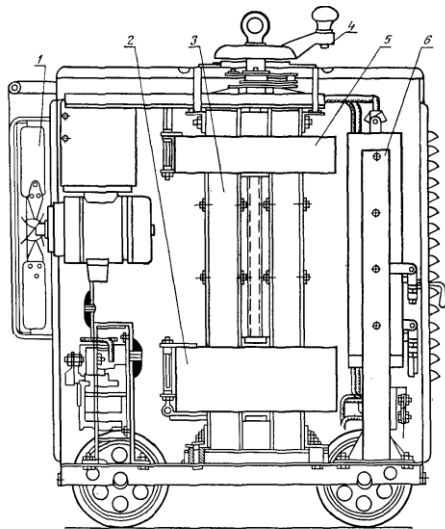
Сварочный выпрямитель ВСС-300:
